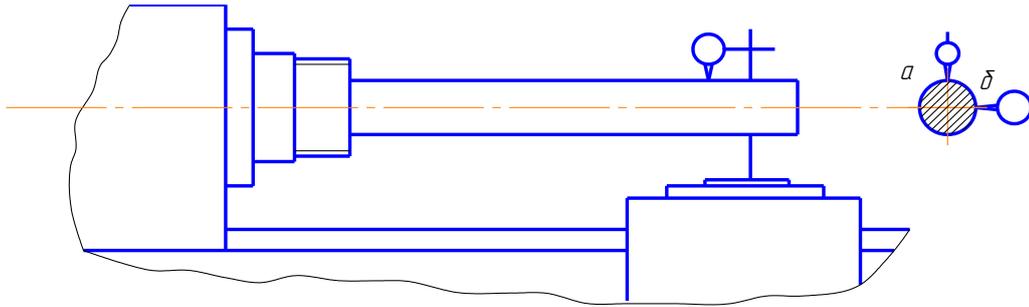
Схема установки индикатора для проверки параллельности оси шпинделя направлению продольного перемещения суппорта
